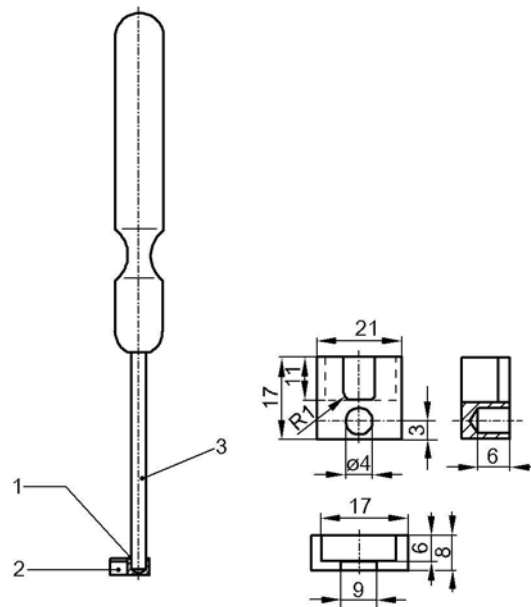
Werkzeug zum Einstecken der Kabelstecker an den Magnetspulen
